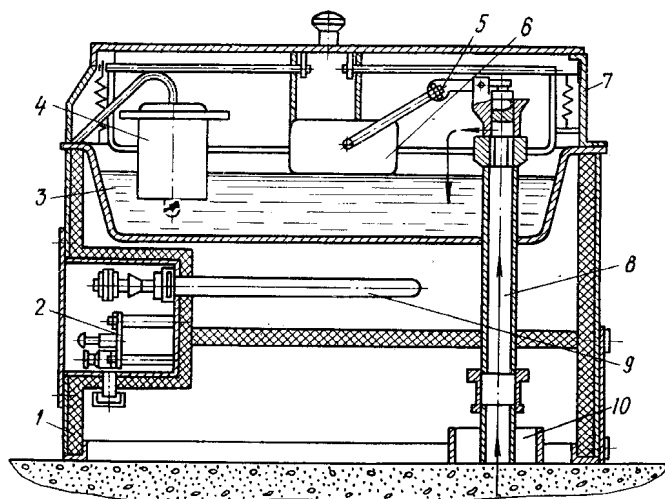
Групова автонапувалка АГК-4А: 1-корпус; 2-реле; 3-чаша; 4-терморегулятор; 5-клапанно-поплачковий механізм; 6-поплавок; 7- кришка; 8- труба для підведення води; 9-нагрівач; 10-стояк.
